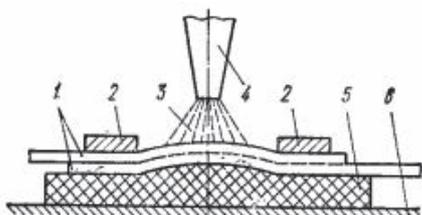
Схема сварки нагретым газом пленочных материалов: 1 – свариваемые пленки, 2 – ограничительные ленты, 3 – струя газа, 4 – наконечник нагревателя, 5 – упругая подложка, 6 – жесткое основание
